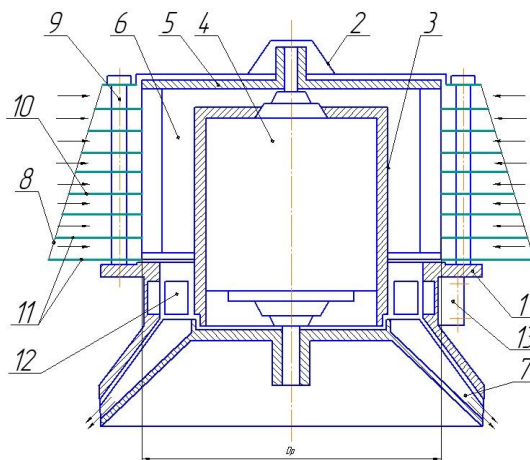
Поздовжній розріз конструкції протипотокового пиловіддільника: 1 - корпус; 2 - захисний кожух; 3 - основа; 4 - електродвигун; 5 - ротор; 6 - лопатки; 7 - робоче колесо; 8 - кільцева решітка; 9 - штифти; 10 - твірна; 11 - кільця решітки; 12 - отвори; 13 - рухоме кільце.
